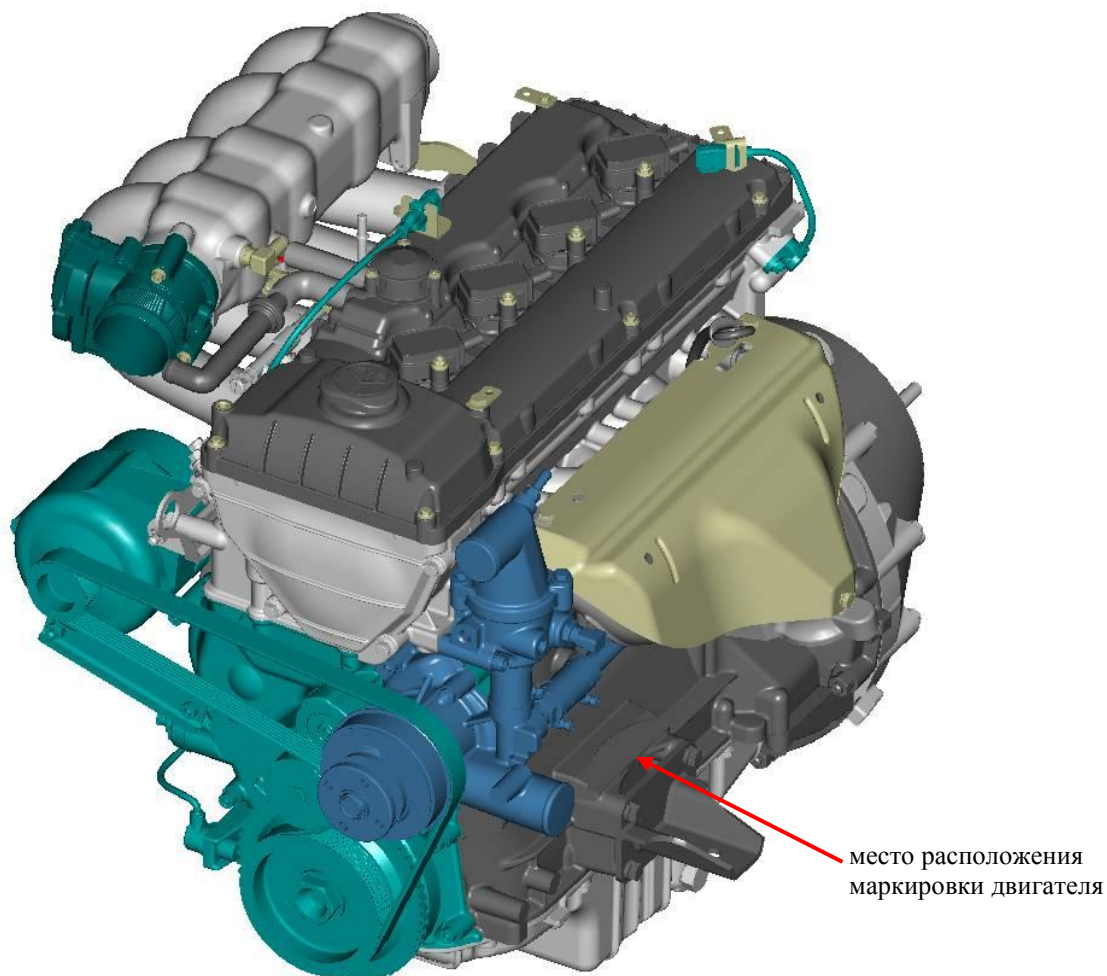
Общий вид двигателя ЗМЗ-40524.10 (экологического класса 4)
